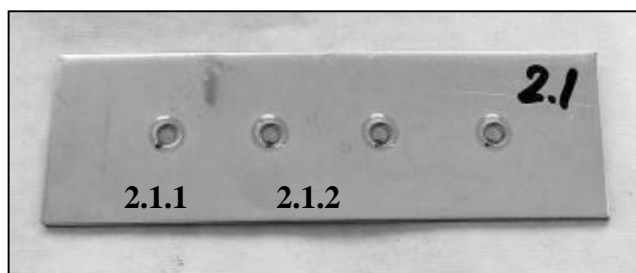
Внешний вид точечной контактной сварки образца № 2.1
